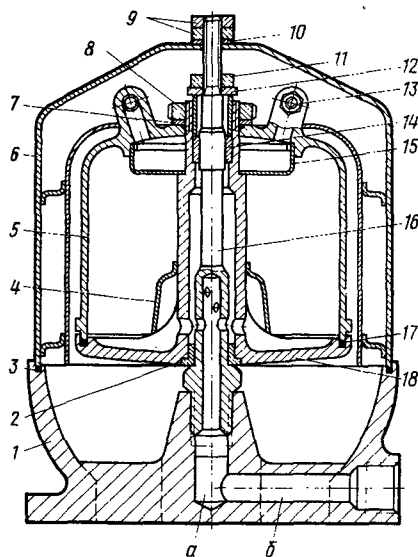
Центробежный масляный фильтр: 1 — основание корпуса; 2, 14 — втулки; 3, 17 — резиновые уплотнительные прокладки; 4 — отражательный кожух; 5 — крышка ротора; 6 — крышка фильтра; 7, 10 — медные уплотнительные кольца; 8, 9, 11 — гайки; 12 — шайба; 13 — сопло; 15 — сетка; 16 — ось; 18 — днище ротора; *a* — центральное отверстие; *b* — горизонтальный канал
